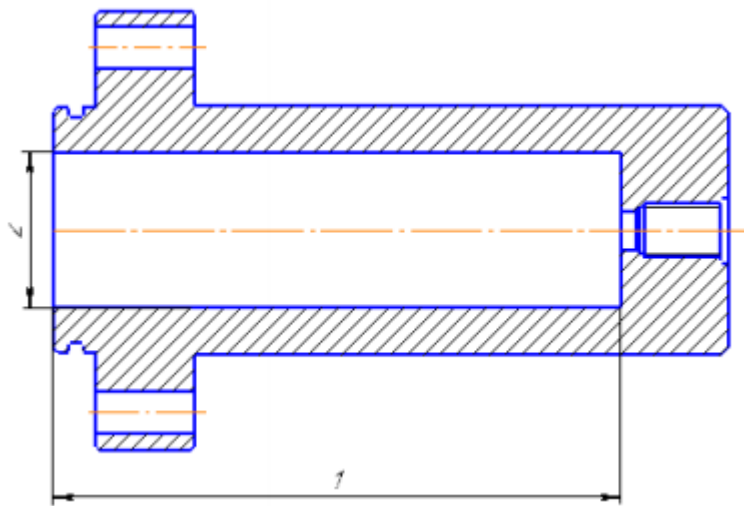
Креслення оброблюваної деталі з необхідними розмірами.
